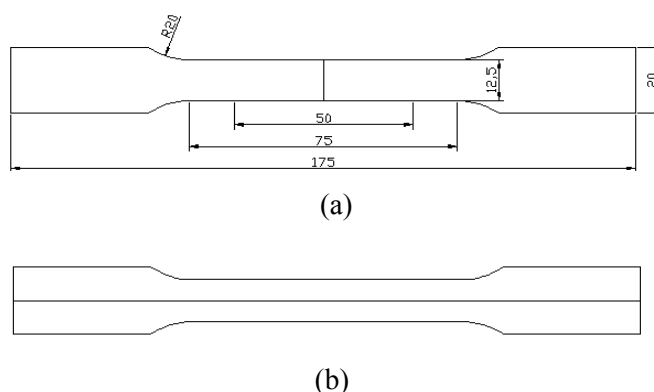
(a) Corpo de prova com cordão de solda na transversal (b) Corpo de prova com cordão de solda na longitudinal (dimensões em mm – NBR 6152)
